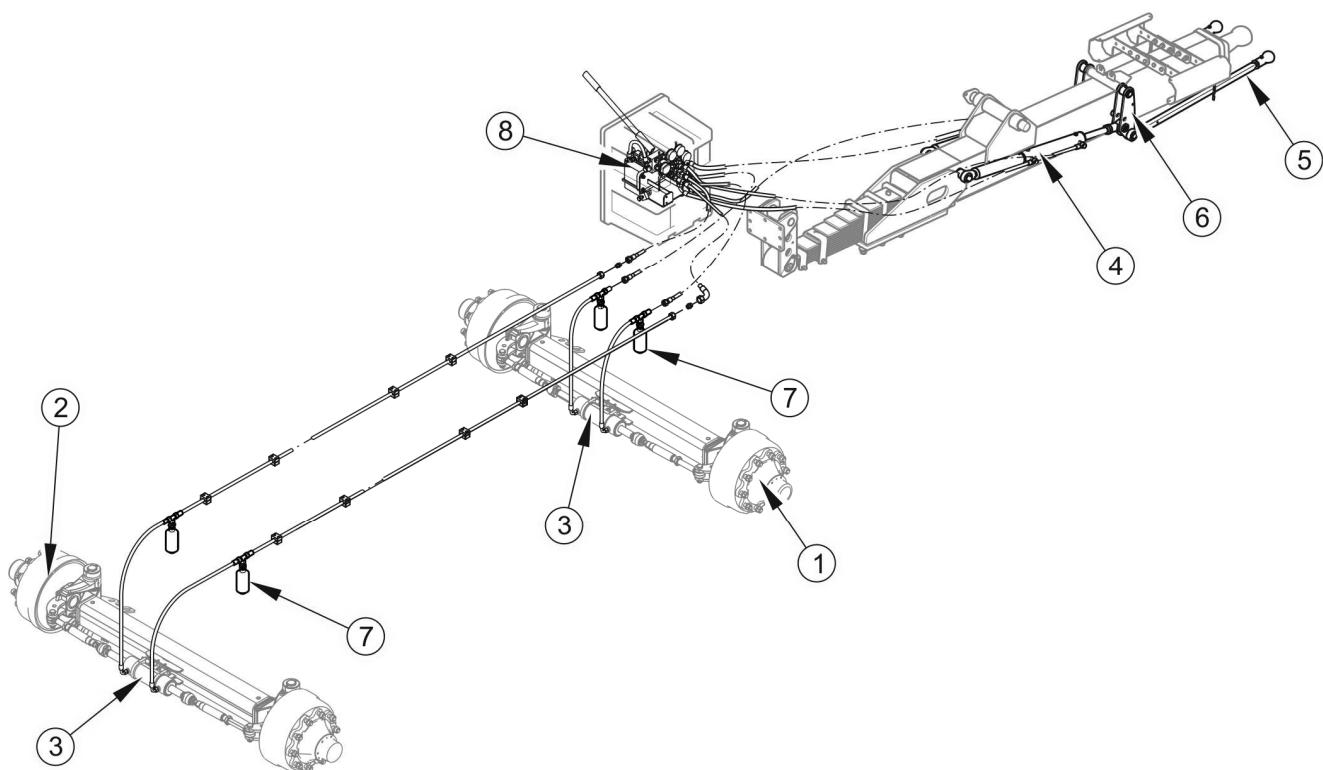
Konstruktion og installation diagram af den hydrauliske bagklap
